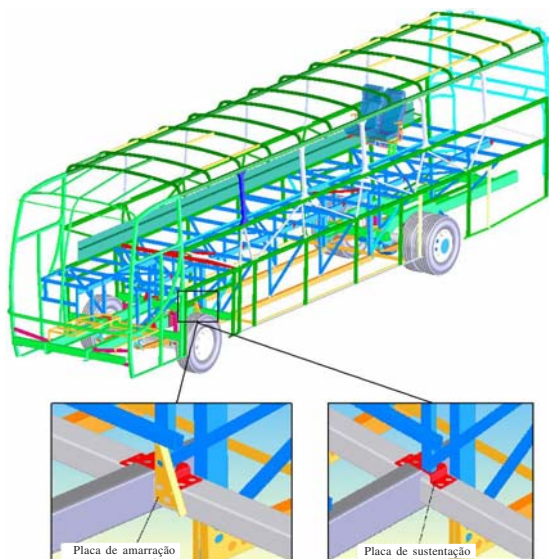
Casulo acoplado ao chassi com placas de amarração e sustentação
